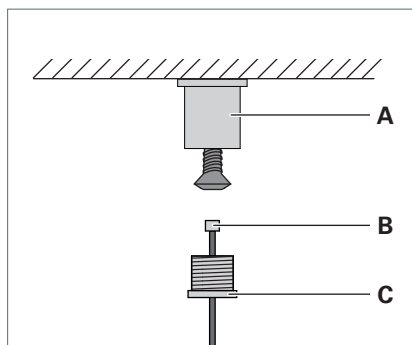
Montaggio dell'elemento di fissaggio al soffitto.
